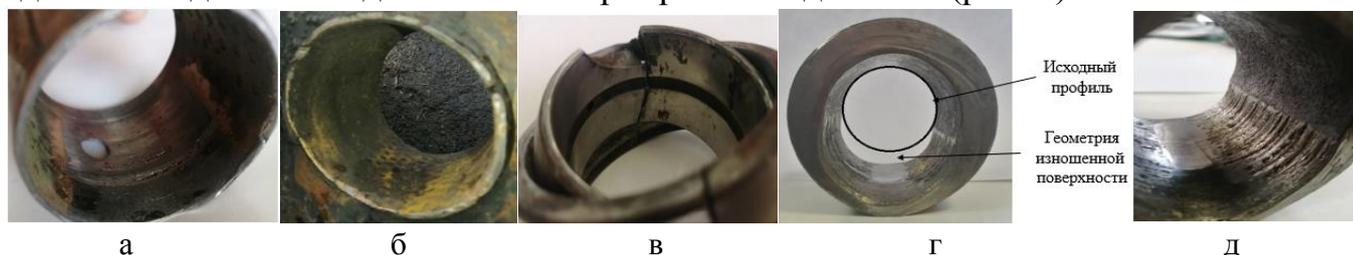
Характерные виды износа деталей шарнирных соединений: а – абразивный износ; б – отслоение упрочняющего покрытия; в – трещины и разрушения; г – износ цилиндрической втулки; д – поверхность изнашивания при 5 кратном увеличении г.
